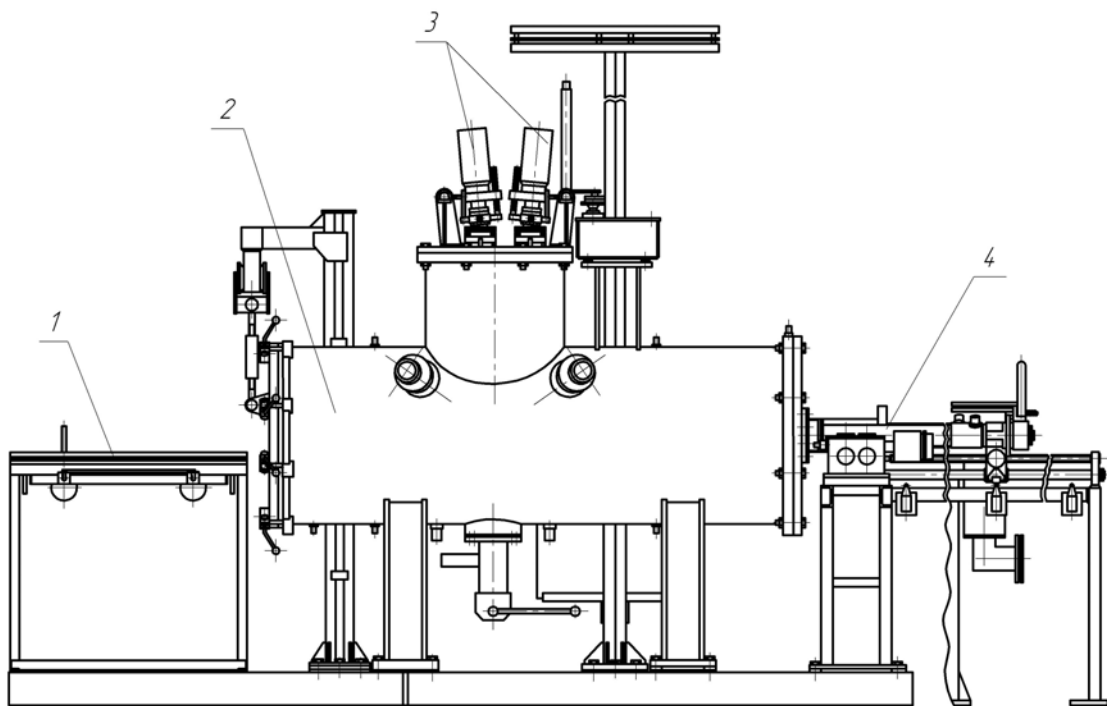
Установку ОБ-1957 для плазово-дугового рафінування поверхні промислових плоских заготовок із прецизійних сплавів:
